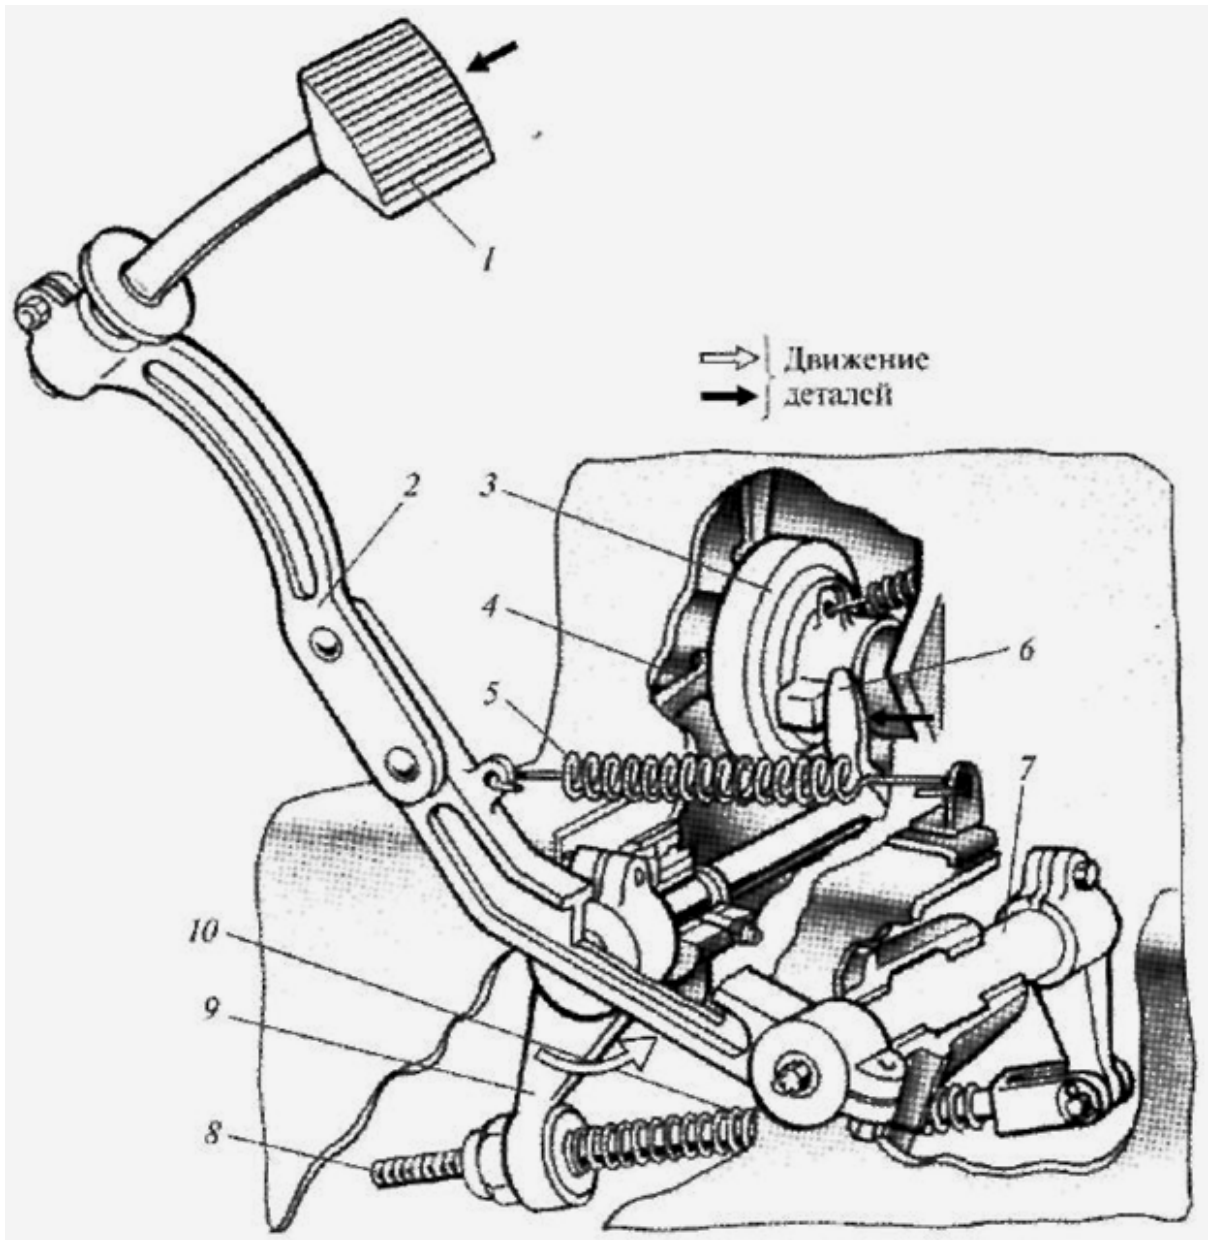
Механический привод выключения сцепления: 1 - педаль сцепления; 2 - рычаг педали; 3 - выжимной подшипник; 4 - отжимной рычажок; 5 и 10 - пружины педали и тяги; 6 - вилка; 7 - вал привода; 8 - тяга; 9 - рычаг вилки
